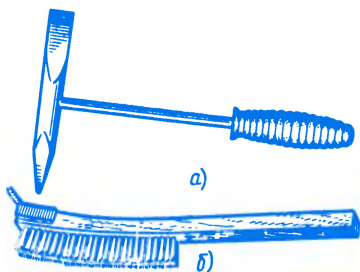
Инструмент для зачистки шва и свариваемых кромок:
